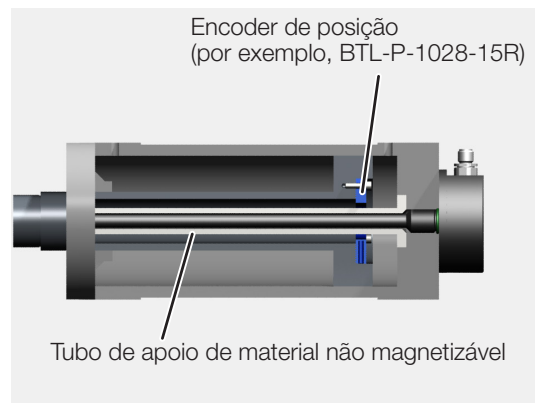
Exemplo 2, BTL instalado com tubo de apoio
